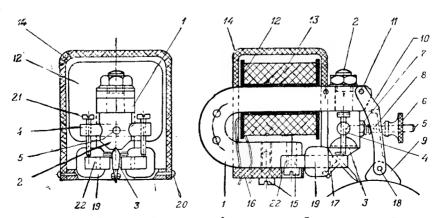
1—электромагнит, 2—упор, 3—вибратор,4—поперечина, 5—регулирующий винт, 6—регулирующая гайка, 7—гайка, 8—пружина, 9—упор, 10—рычаг, 11—шпилька, 12—катушка подмагничивания, 13—обмотка 0,07, 14—коробка, 15—винт, 16—накладка, 17—зажимный винт, 18—шпилька, 19—звуковая обмотка, 20—крепящие винты, 21—регулировочный винт, 22—сердечник
